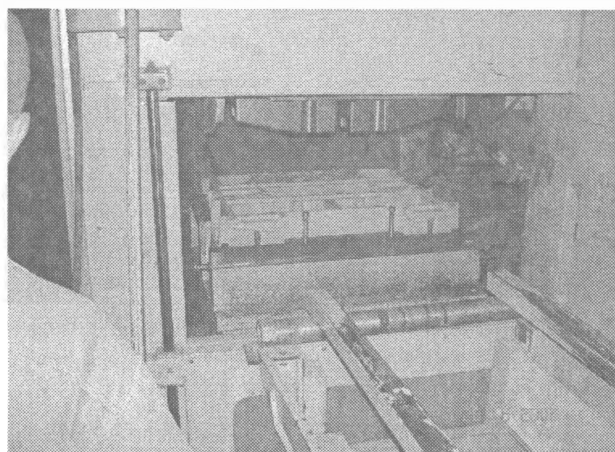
Изготовление стержней по Cold-box-amin-процессу для отливки «Балка надрессорная»
